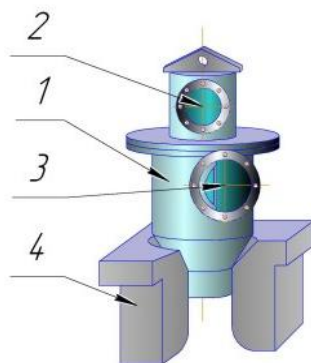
Конструкция камерного зажигательного горна с торцевыми горелками
